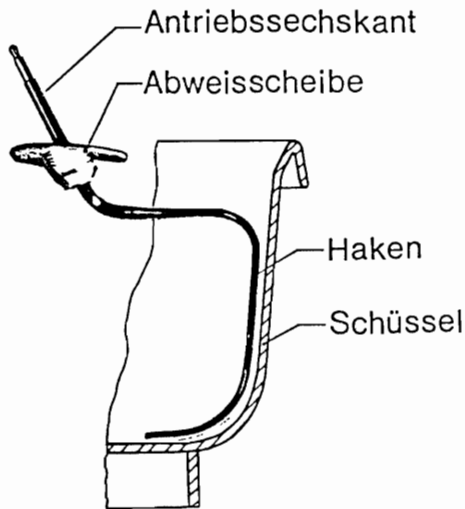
/29: Knetwerkzeug mit Schüssel einer Klein-Küchenmaschine (Vertikal-Teilschnitt)
